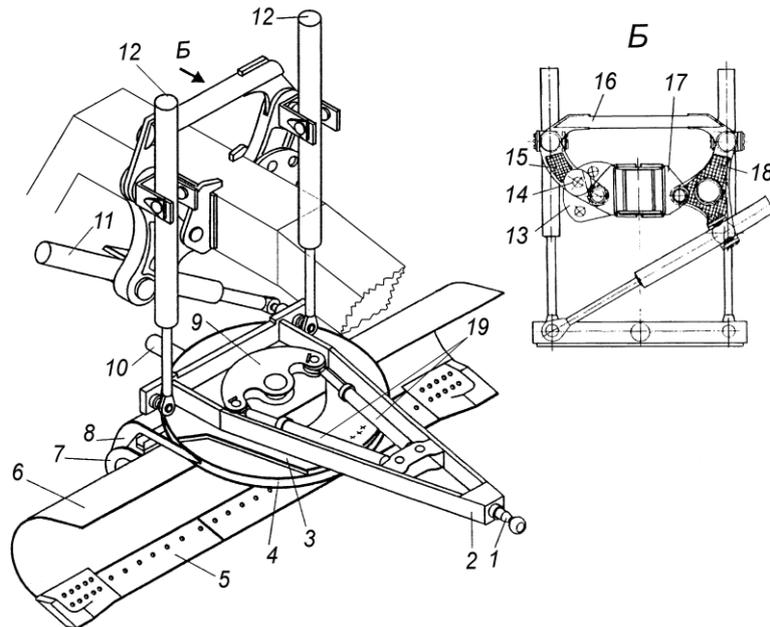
Рабочее оборудование автогрейдера А120: 1 – шкворень; 2 – несущая балка; 3 – опорный лист несущей балки; 4 – поворотный круг; 5 – нож; 6 – отвал; 7 – опора отвала; 8 – кронштейн поворотного круга; 9 – щека поворотного круга; 10 – гидроцилиндр изменения угла резания; 11 – гидроцилиндр выноса тяговой рамы; 12 – гидроцилиндры подъема-опускания отвала; 13, 17 – кронштейны подвески; 14 – поршень-защелка; 15 – левый рычаг; 16 – тяга; 18 – правый рычаг; 19 – гидроцилиндры поворота отвала
